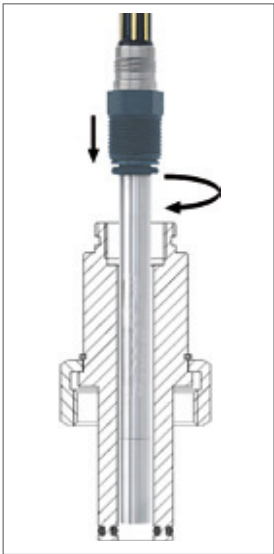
Raccordo di montaggio 25 mm su PG 13,5
